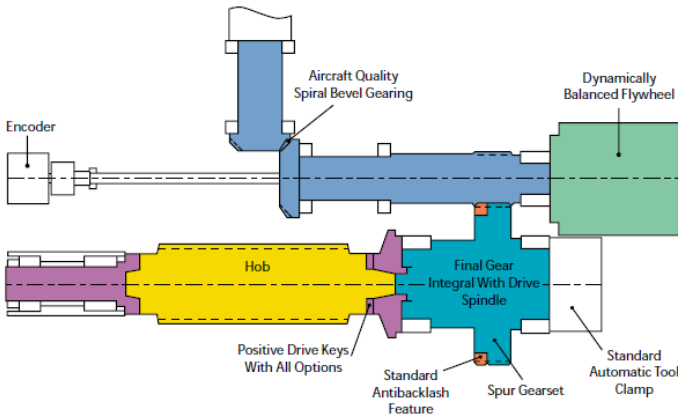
Компонування зубофрезерного верстата з ЧПК 125GH фірми Gleason
